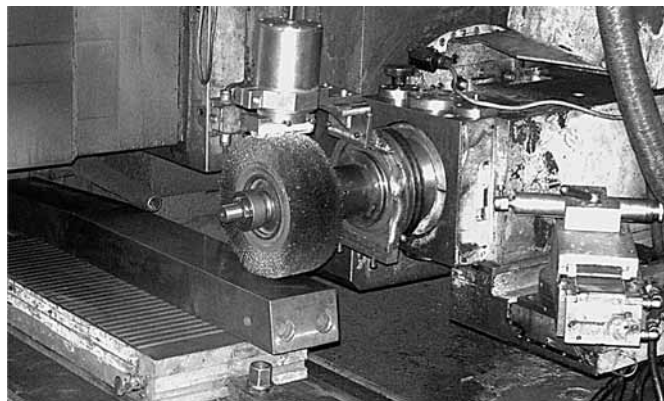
Устройство для формирования покрытия на рабочей поверхности оправки подпрессорника
